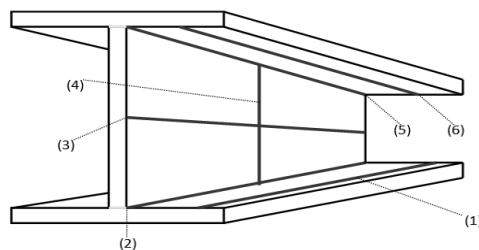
17 Clasificación del cordón de soldadura según la posición.
